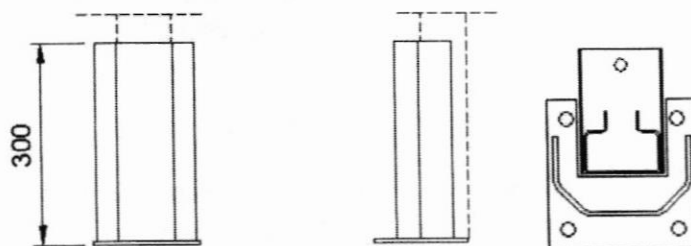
Protetor de coluna (vistas frontais e planta (ABNT NBR 15524-1).
